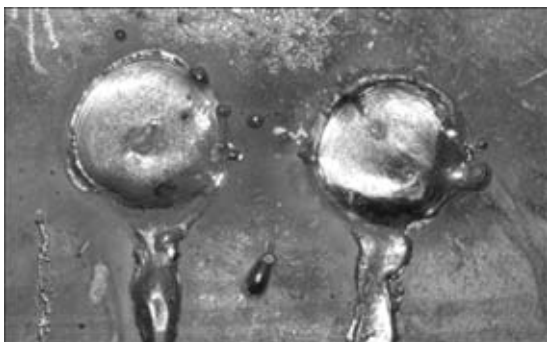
Внешний вид точки при сварке на вертикальной плоскости со стеканием расплавленного металла и неодинаковым формированием точечного соединения
